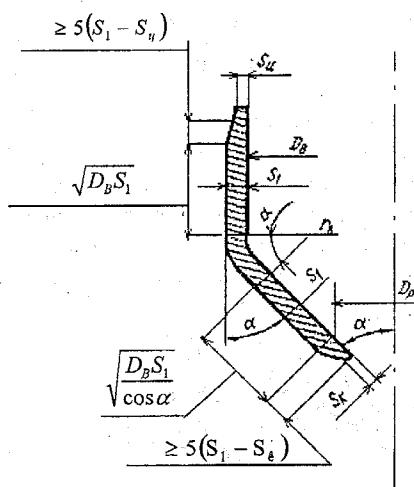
Розрахункова схема до визначення товщини стінки конічного відбортованого днища
